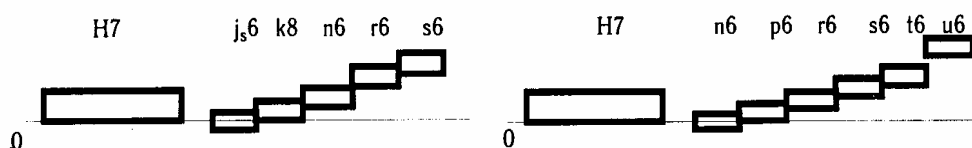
Поля допусков отверстия в корпусе и вкладыша (втулки)
